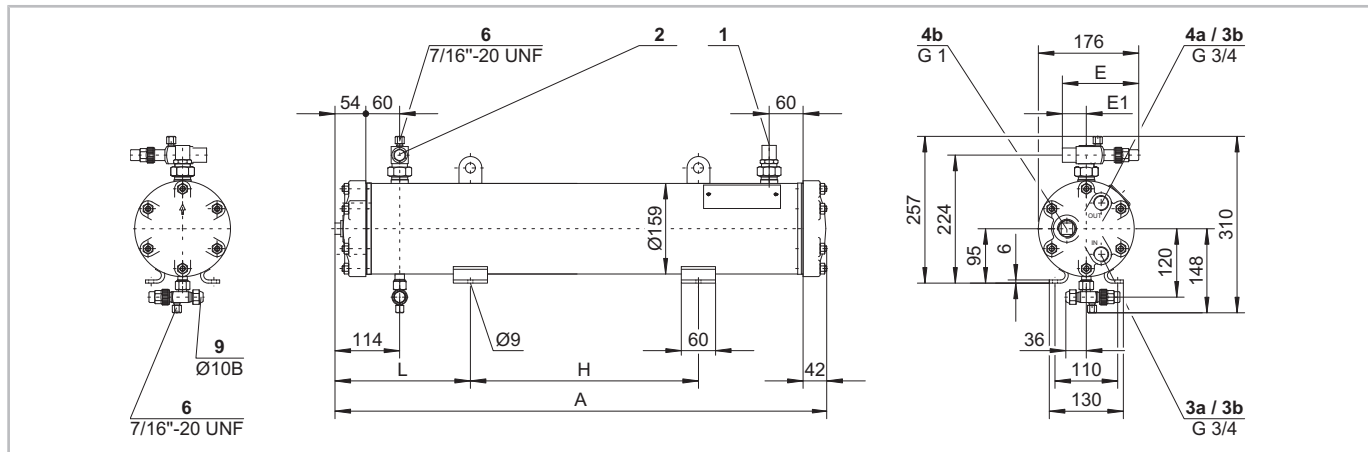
Maßzeichnungen Ölkühler OW401, OW 501
